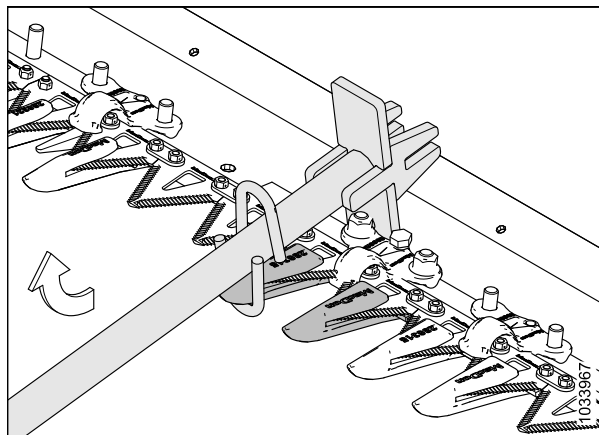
Регулировка смещением вверх — заостренный противорезающий палец
